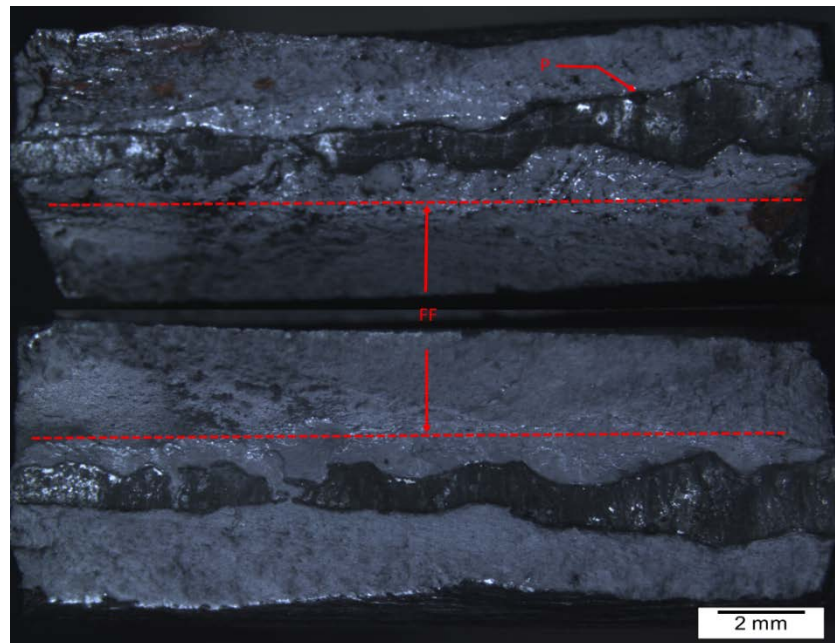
Imagen por estereoscopio de la fractura del ensayo de tensión T2 unión soldada ER312.
